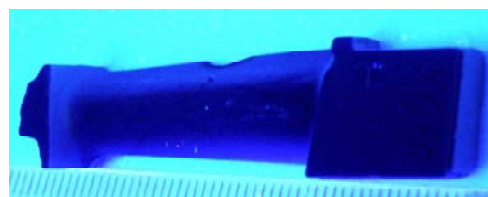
Внешний вид опытной литой рабочей лопатки из сплава ЖС26-ВИ (ВНК)
